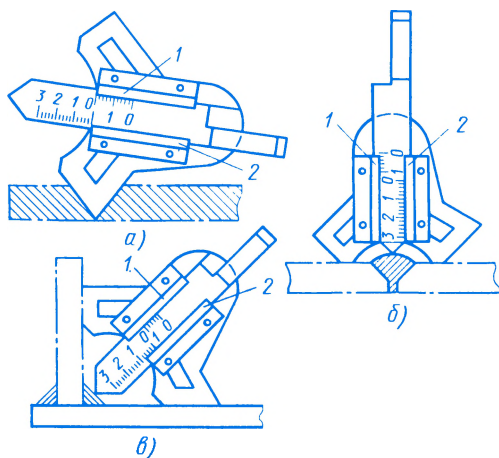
Универсальный измеритель швов: а — проверка угла скоса кромок, б — проверка величины превышения усиления шва, в — проверка высоты углового шва; 1 — шкала выпуклости стыкового шва, 2 — шкала высоты углового шва
